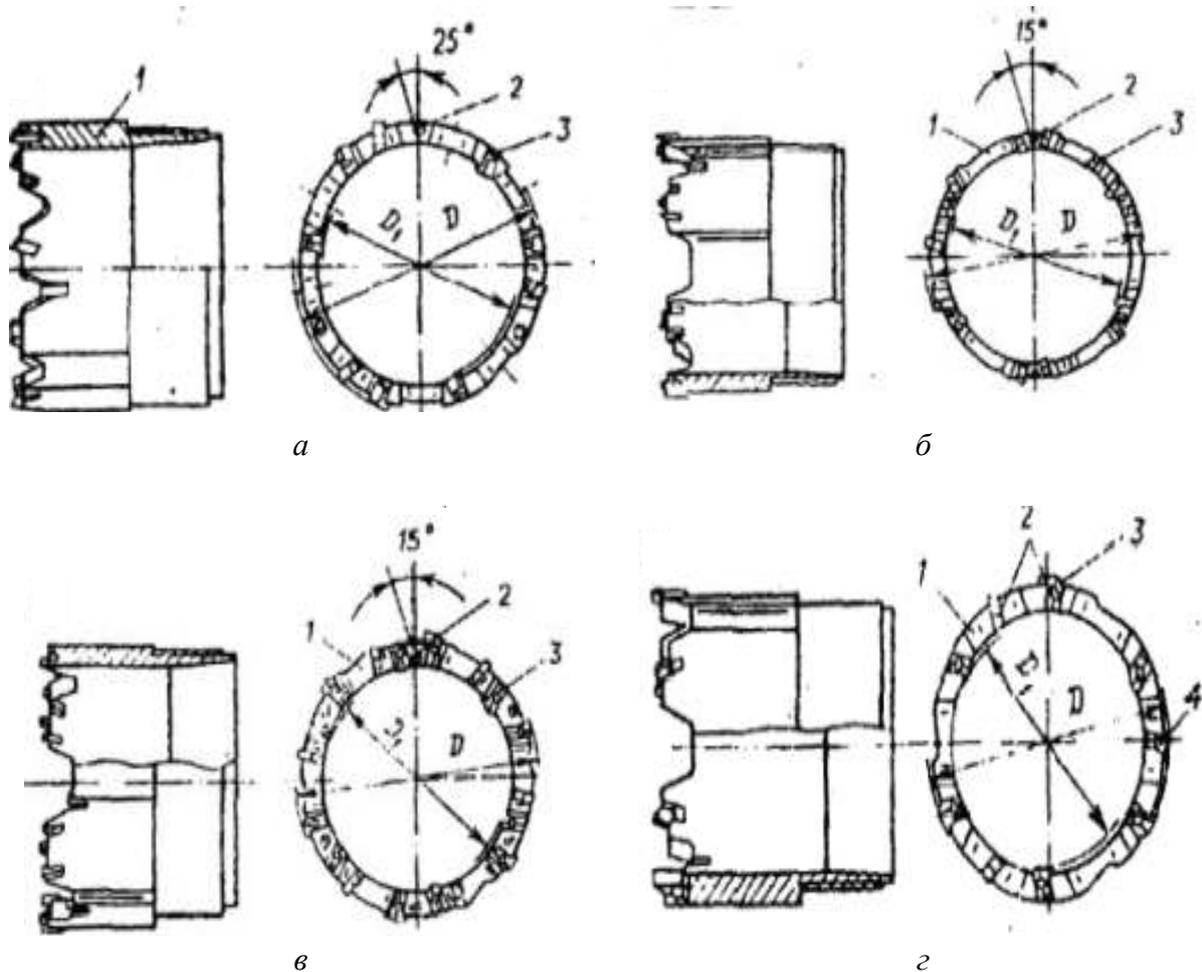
Резцовые коронки: *а* – СМ4; *б* – СМ5; *в* – СМ6; *г* – СТ2: 1 – корпус; 2, 4 – резцы; 3 – вкладыши
